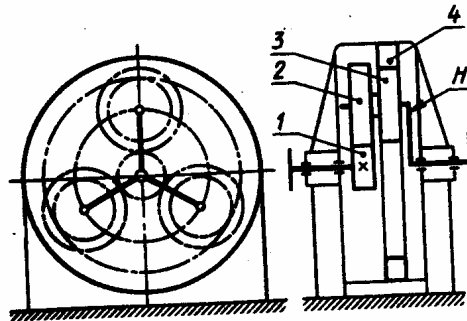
(б). Кинематическая схема планетарного двухступенчатого редуктора с ведомым водилом:
